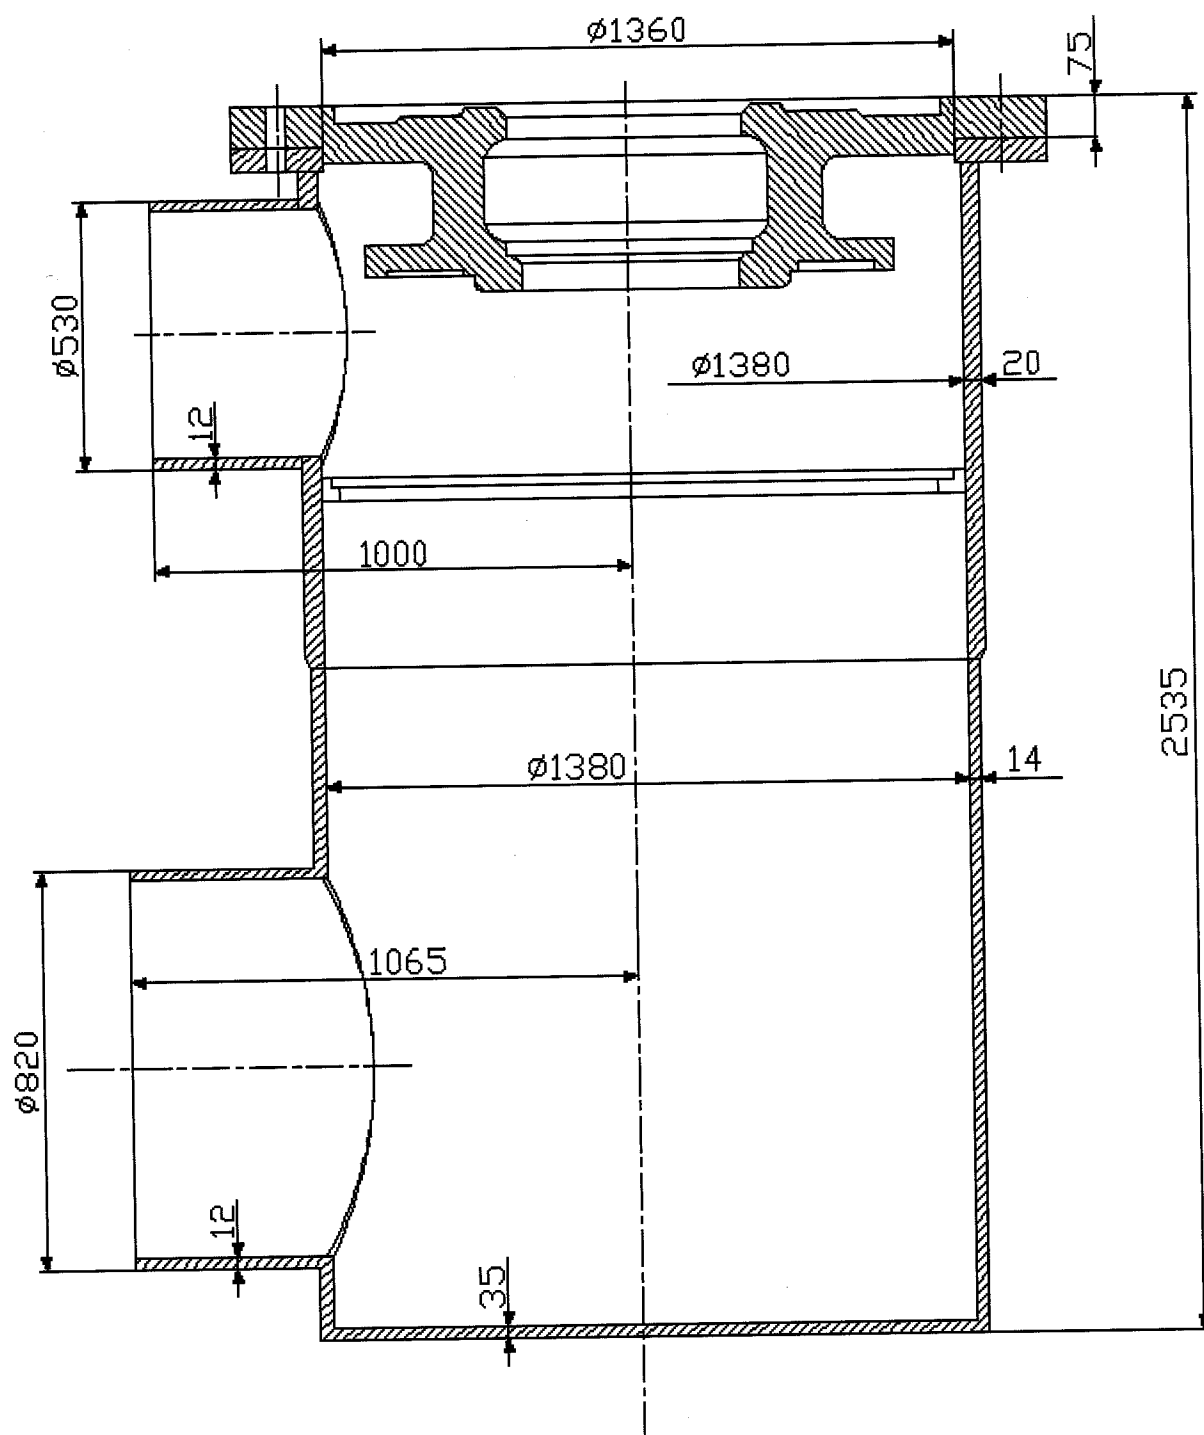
Эскиз корпуса насоса в сборе с крышкой
